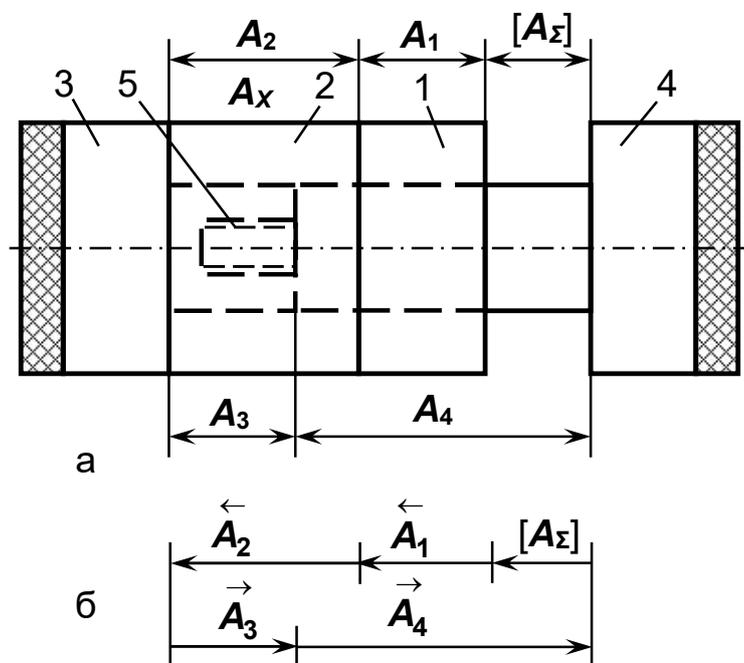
Эскиз сборочного узла (а) и схема размерной цепи (б): 1, 2 – втулки; 3, 4 – ступенчатые валы; 5 – резьбовое соединение
